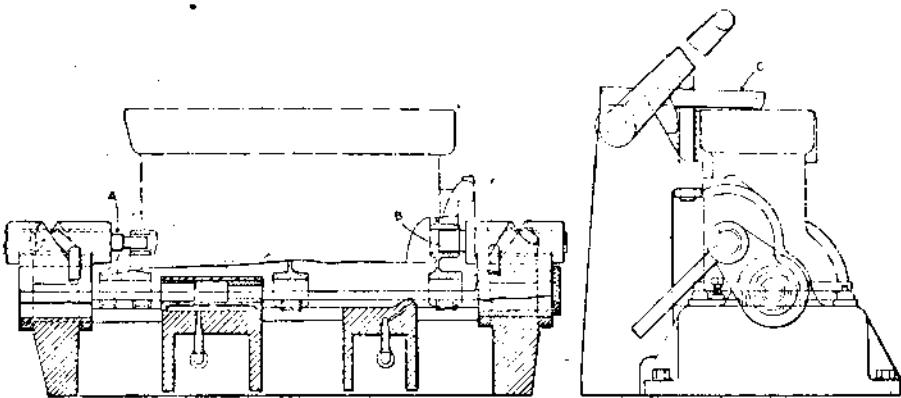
Расточка подшипников коленчатого вала двумя зенкерами
